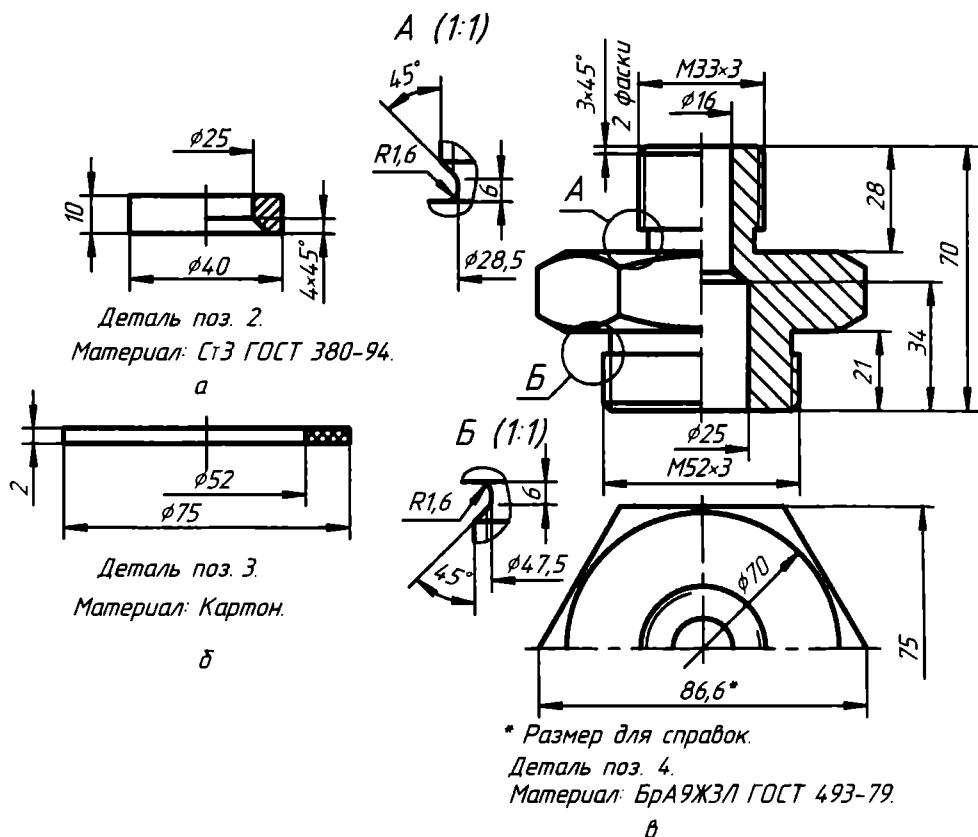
Чертежи: а — седла; б — прокладки; в — штуцера
